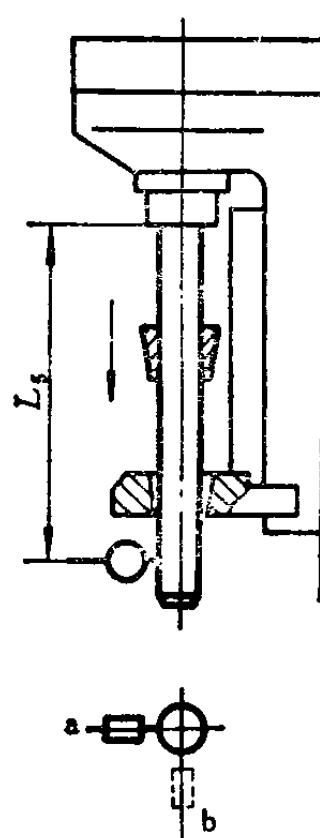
活动轴承座的轴承孔与刀具主轴轴线的同轴度的检验
